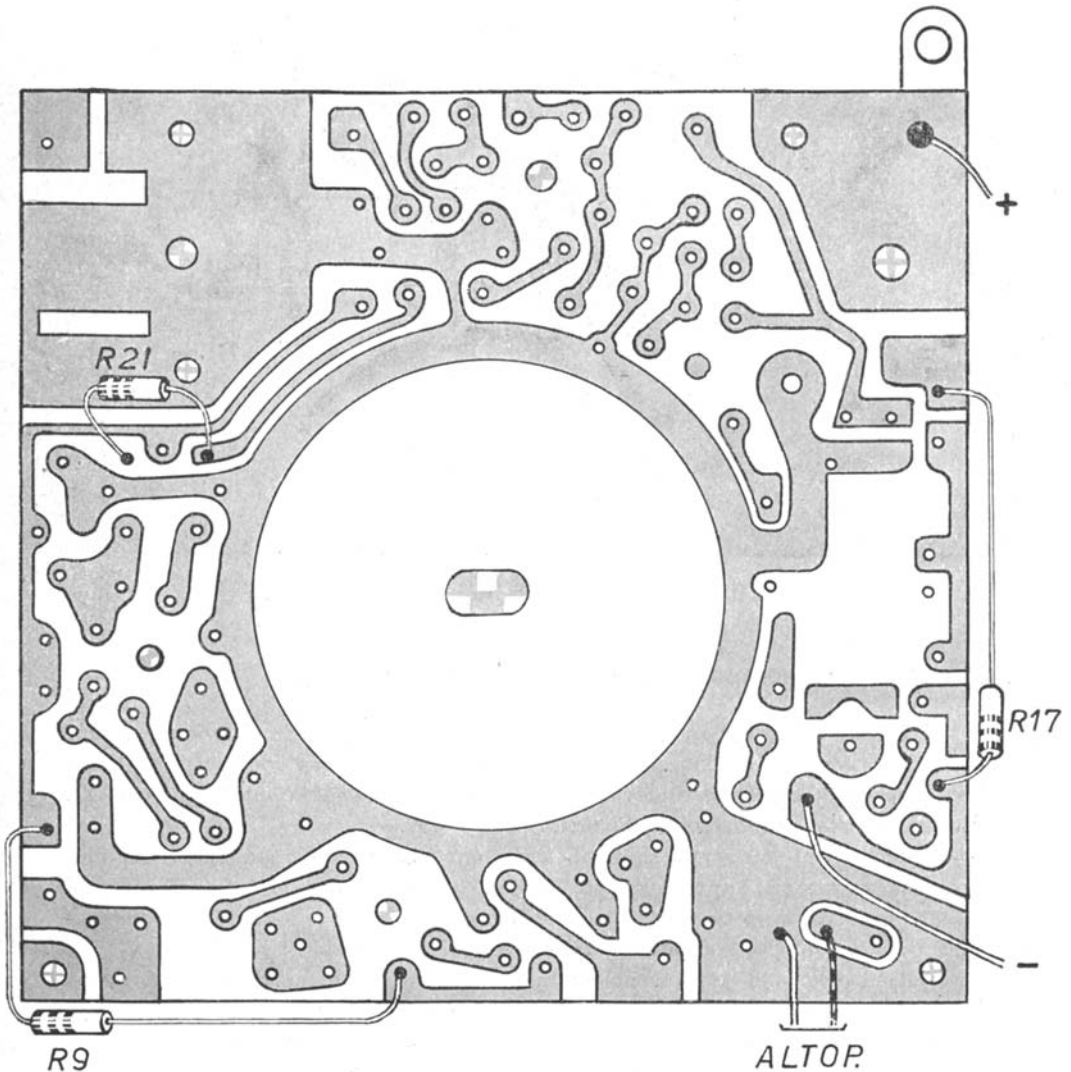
Pannello con tutto il cablaggio stampato di un apparecchio di produzione commerciale.
